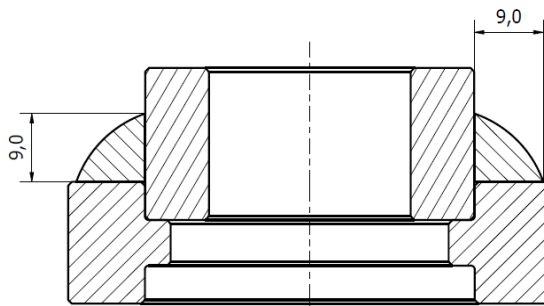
Especificação dimensional do cordão de solda (tamanho mínimo)
